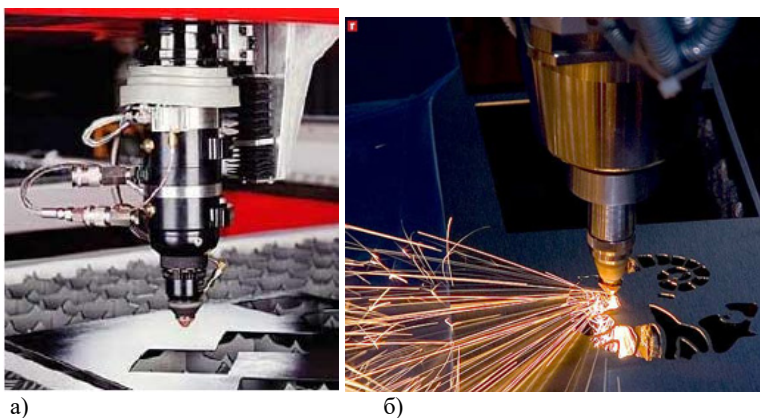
Головка для лазерной резки (а) и процесс лазерной резки (б)
